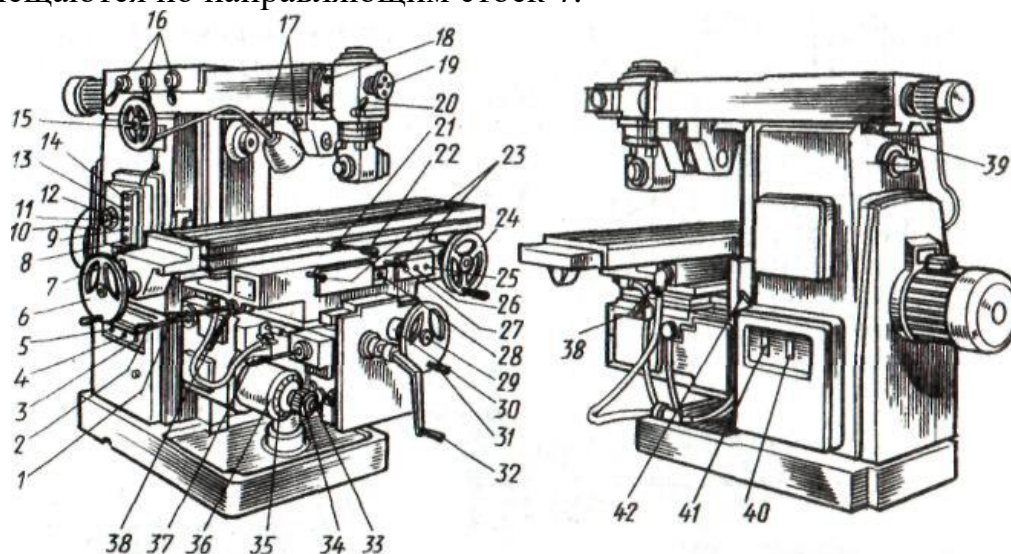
Общий вид станка мод. 6P82Ш:
